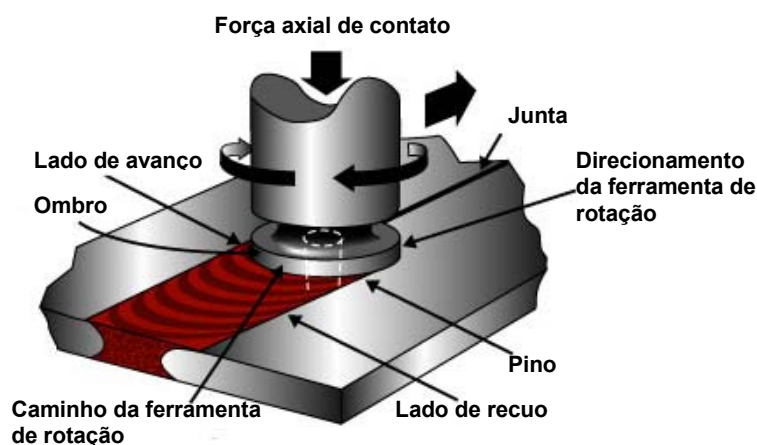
Ilustração geral do processo de friction stir welding.
